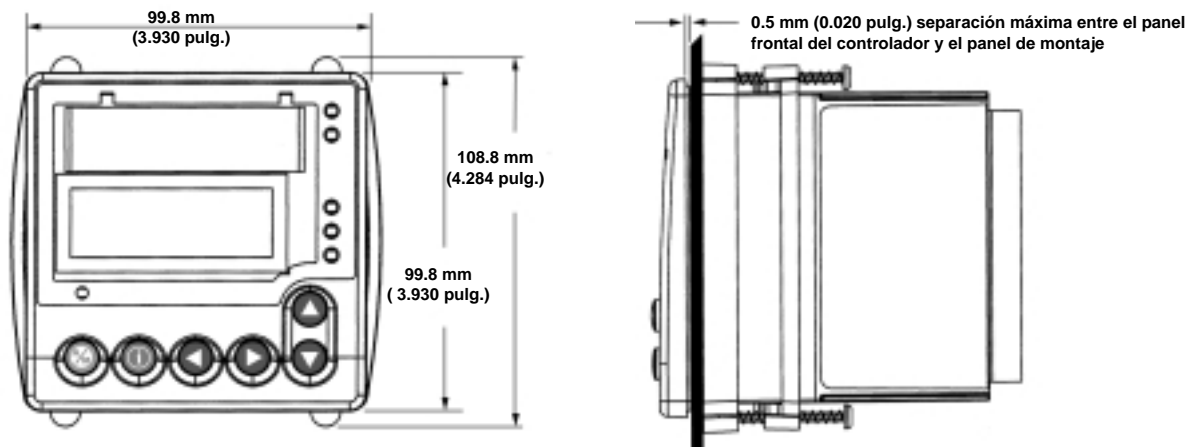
Dimensiones de la vista frontal y dimensión de la separación para la junta.
